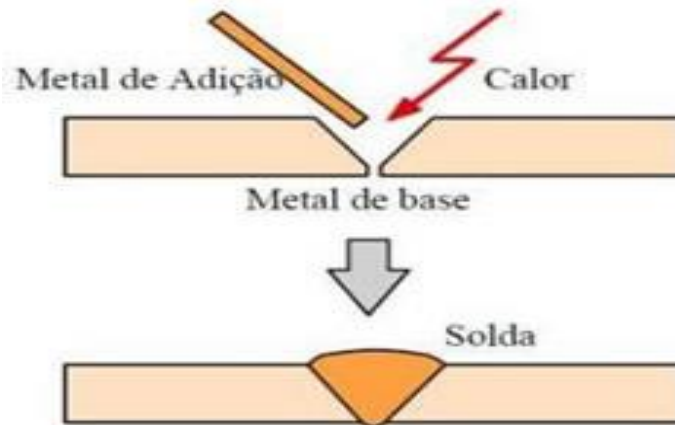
Demonstração ilustrativa do processo de soldagem por fusão
